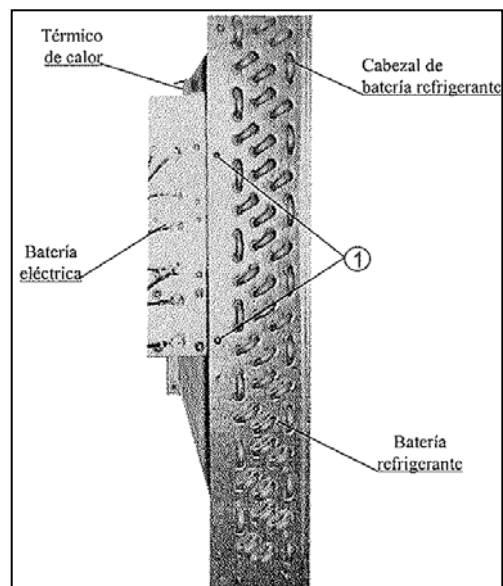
Sujeción de Batería Eléctrica a la Batería Refrigerante.
